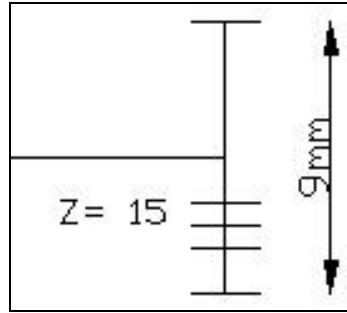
Dimensiones del engranaje del motor de pasos.
